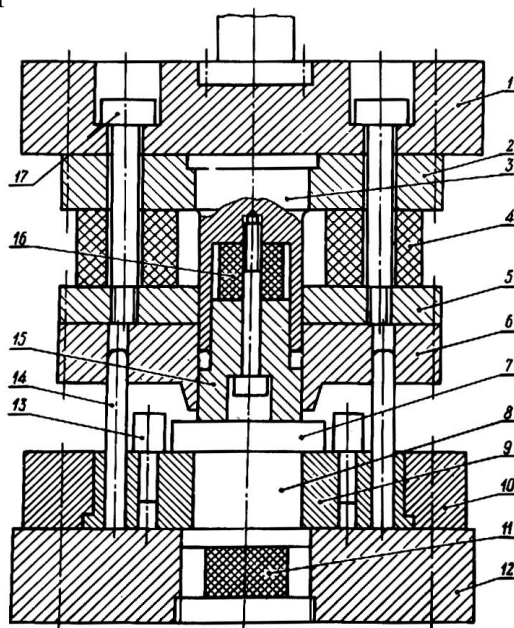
Схема штампа для чистовой вырубki биметаллов
